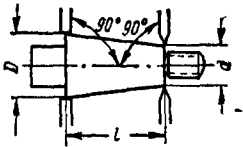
Схема проверки размеров конической поверхности губками штангенциркуля.
